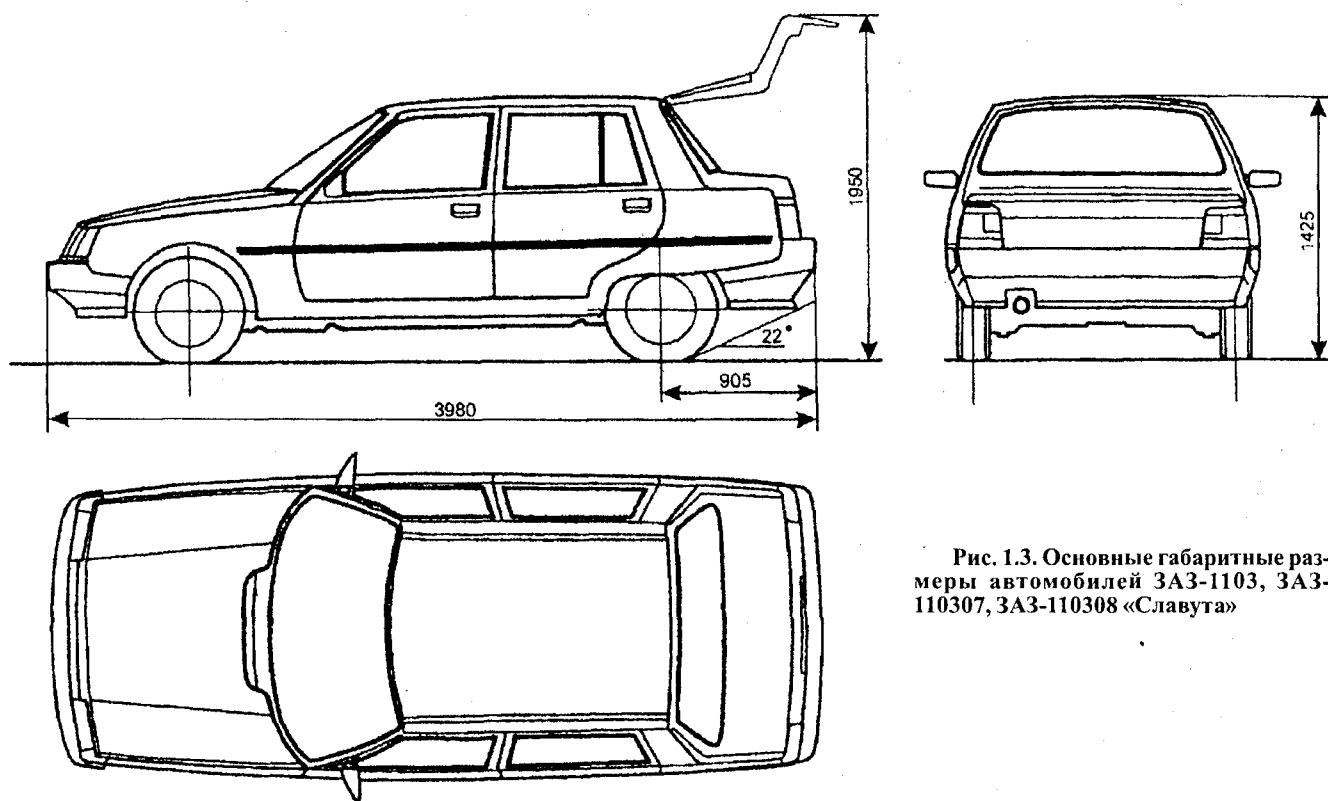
Основные габаритные размеры автомобилей ЗАЗ-1103, ЗАЗ-110307, ЗАЗ-110308 «Славута»
